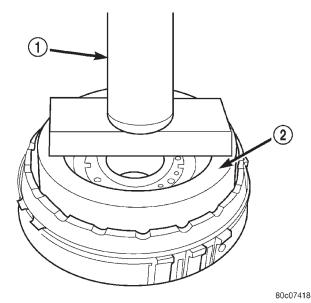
Compresión del muelle Belleville del embrague de 2^a con la herramienta 8249
